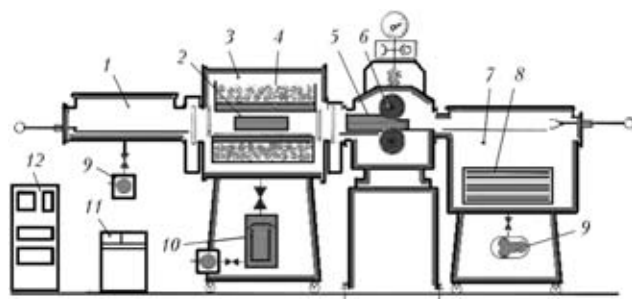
Схема вакуумного прокатного стана для соединения разнородных материалов в твердой фазе [14]: 1 — камера загрузки; 2 — свариваемый пакет пластин в печи; 3 — вакуумная печь; 4 — керамический изолятор; 5 — свариваемый пакет пластин в валковой камере; 6 — валки; 7 — камера выгрузки и сбора готовой продукции; 8 — готовая продукция в сборнике проката; 9, 11 — стойки управления технологическим процессом прокатки; 10 — вакуумная система, состоящая из диффузионного и форвакуумных насосов; 12 — автоматизированная система контроля и управления технологическим процессом прокатки
